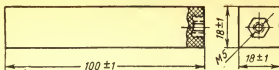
Габаритный чертеж столбов Д1005, Д1006, Д1007, Д1008.
